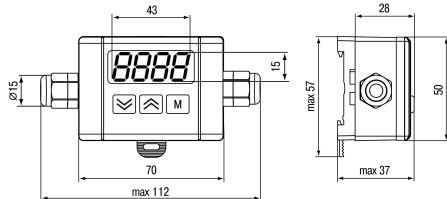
Габаритные размеры корпуса НЗ
